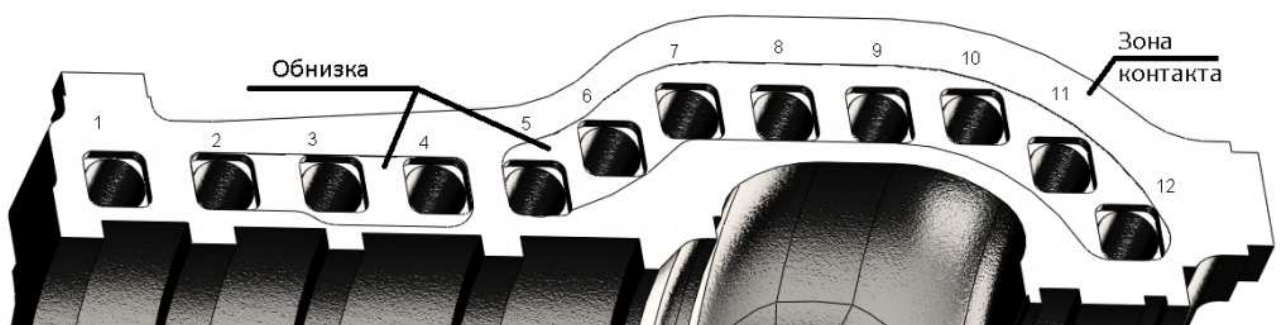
Внутрішній корпус ЦВТ (дзеркало фланцевого роз'єму)
